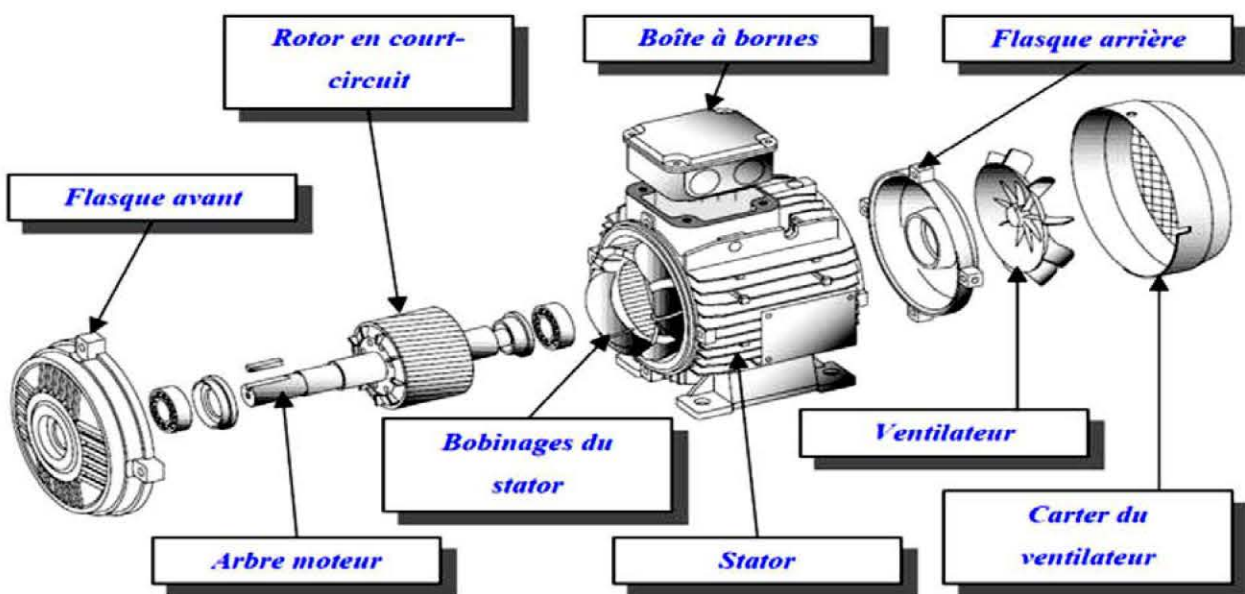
Vue éclatée d'un moteur asynchrone à cage d'écureuil [6]
